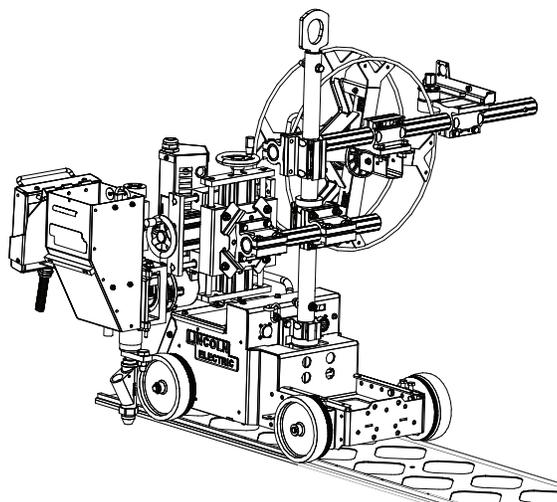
VISTA TRASEIRA SOLDAGEM CONTÍNUA
